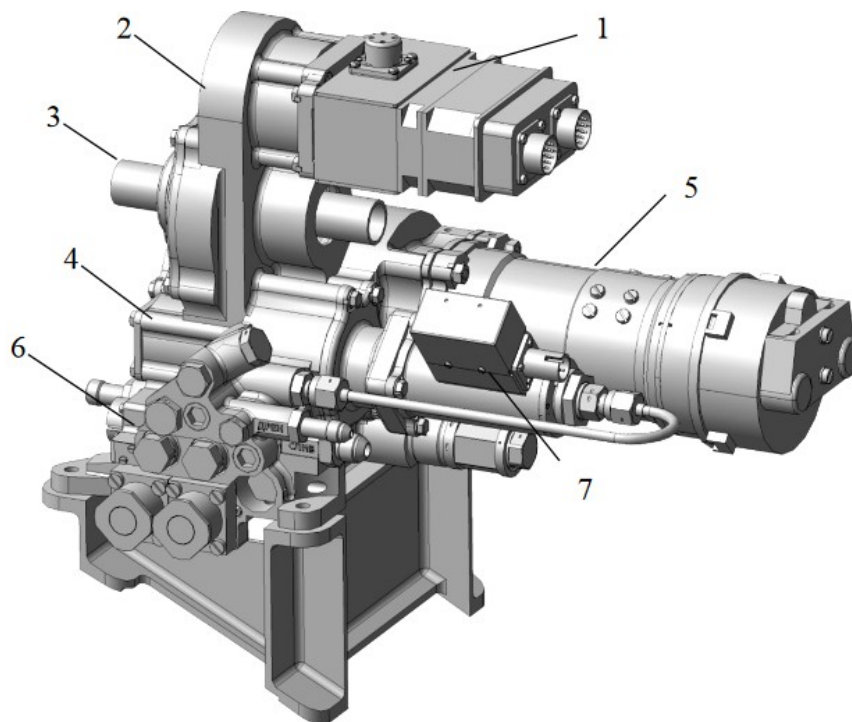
Загальний вигляд комбінованого приводу механізації (1 – блок мікроперемикачів, 2 - планетарний редуктор, 3 - вихідний вал, 4 - гідромотор реверсивний, 5 – електродвигун, 6 – блок гідро керування , 7- гальмо гідравлічне).
